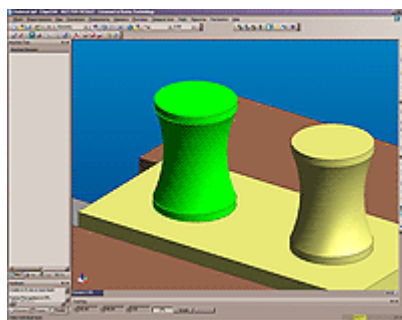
Определение обрабатываемых поверхностей с помощью команды Набор поверхностей.
